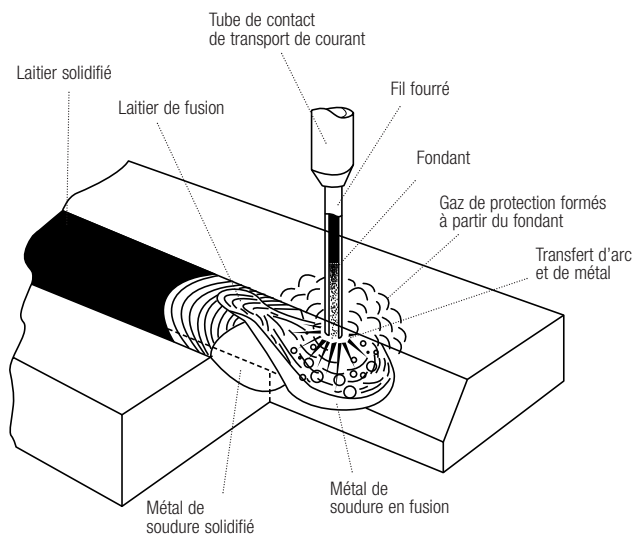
Arrangement de soudage à l'arc avec fil fourré (FCAW)
